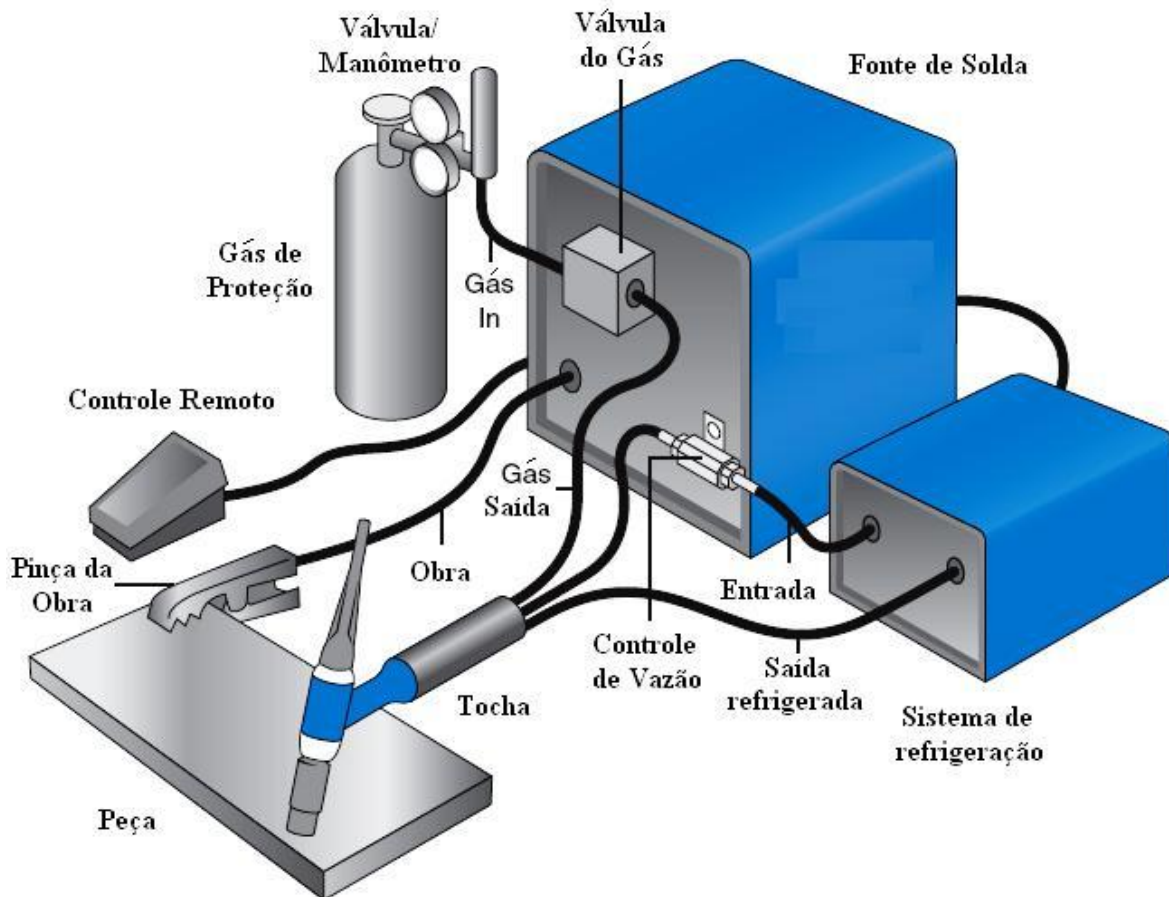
Equipamentos básicos para soldagem TIG (Miller, 2006).
